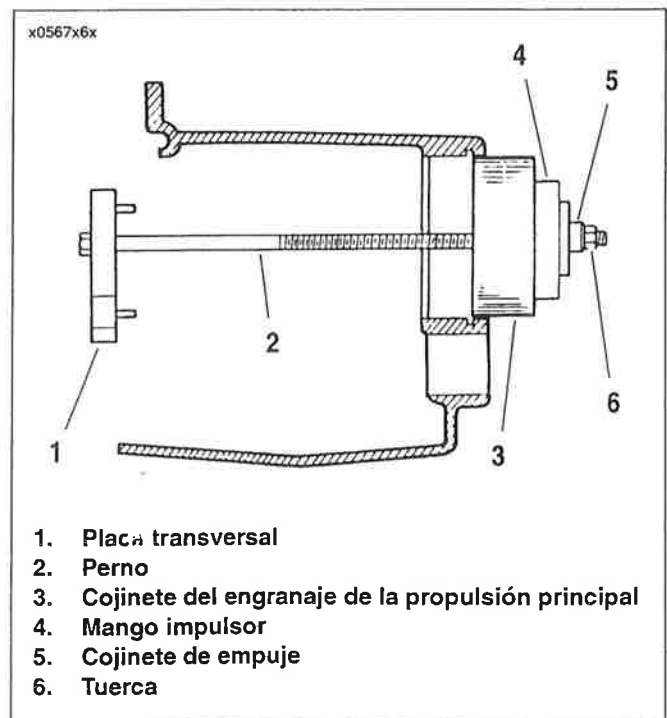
Extractor de cojinetes Montaje de placa transversal (pieza N° B-45847)
